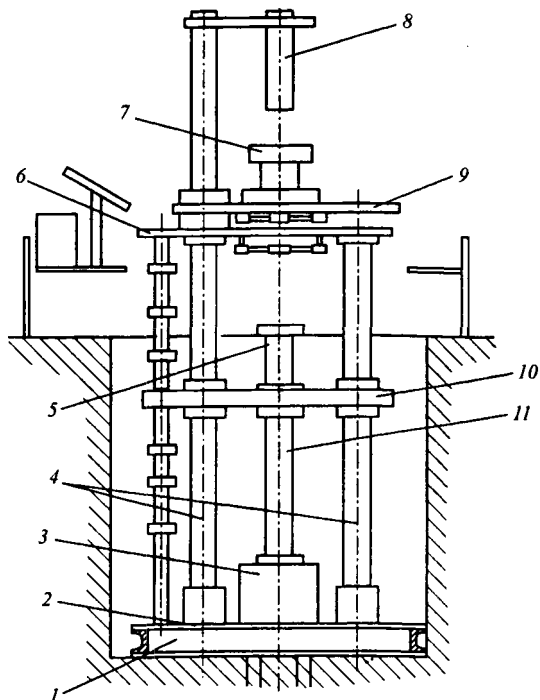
Схема установки вертикального непрерывного литья модели МУ115:
